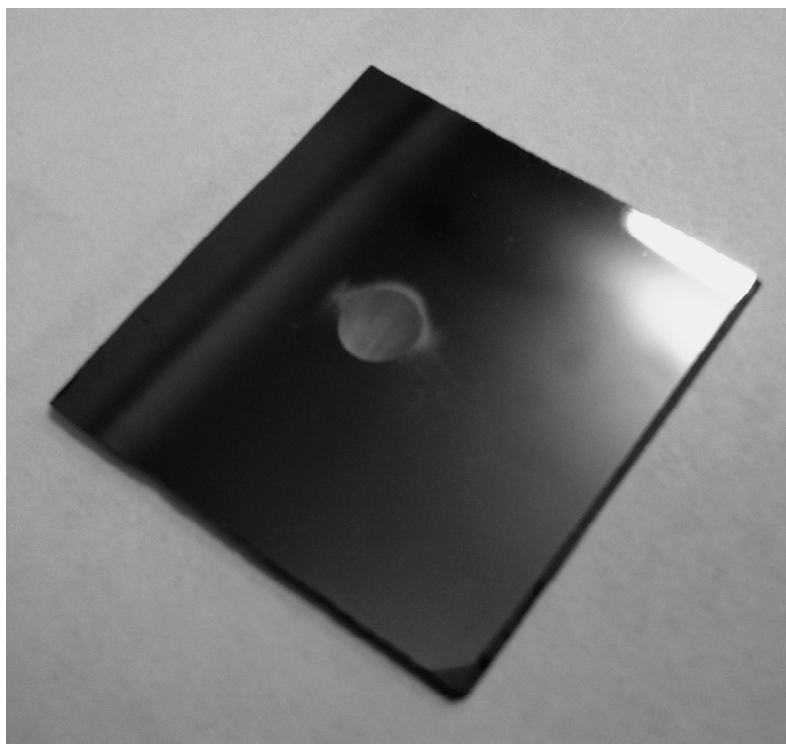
Внешний вид шлифа на поверхности полупроводниковой пластины
